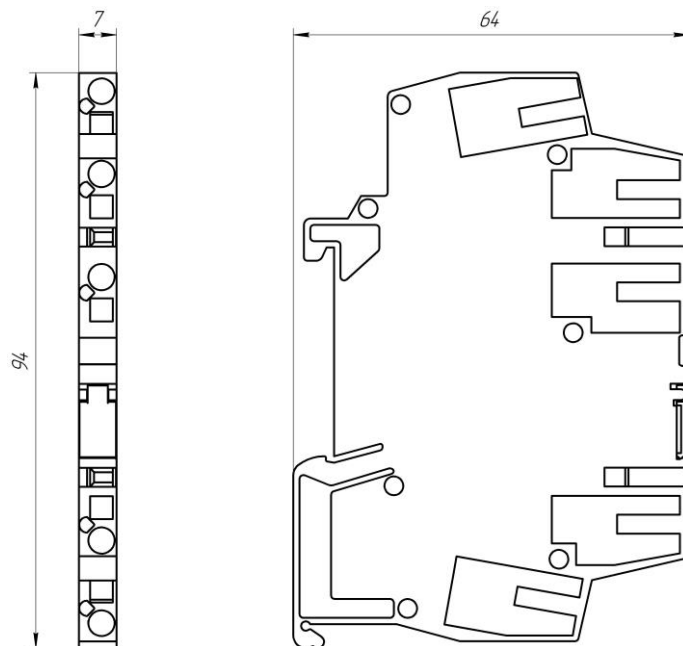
Внешний вид и габаритные размеры преобразователя ПНС-652
